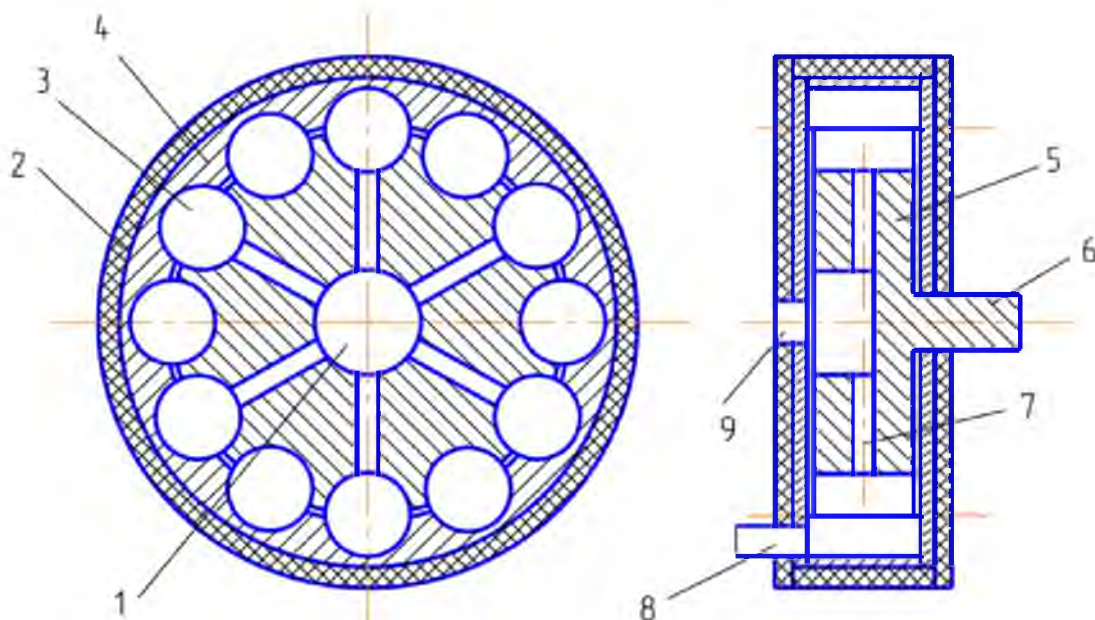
/8/ - Схема гідродинамічного нагрівача: 1 – розточка ротора; 2 – термоізоляція; 3 – комірка; 4 – корпус; 5 – ротор; 6 – вал; 7 – радіальний канал; 8, 9 – отвори введення та виведення молока
